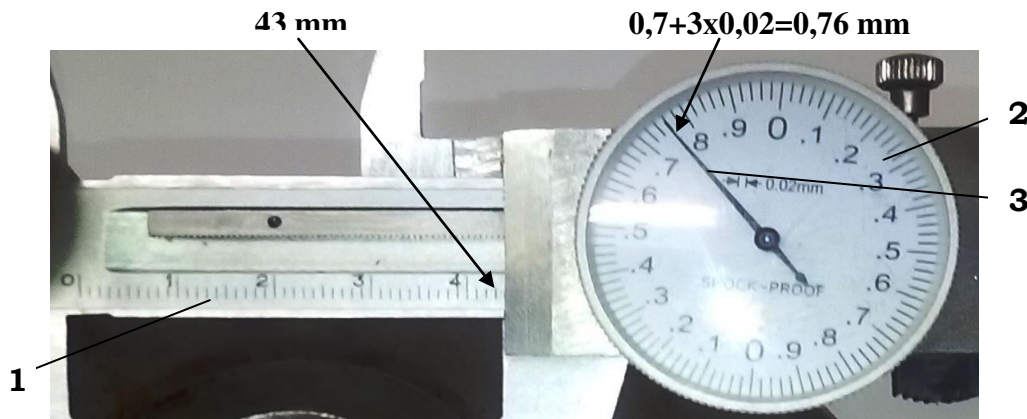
Citirea dimensiunii măsurate cu șubler cu vernier
